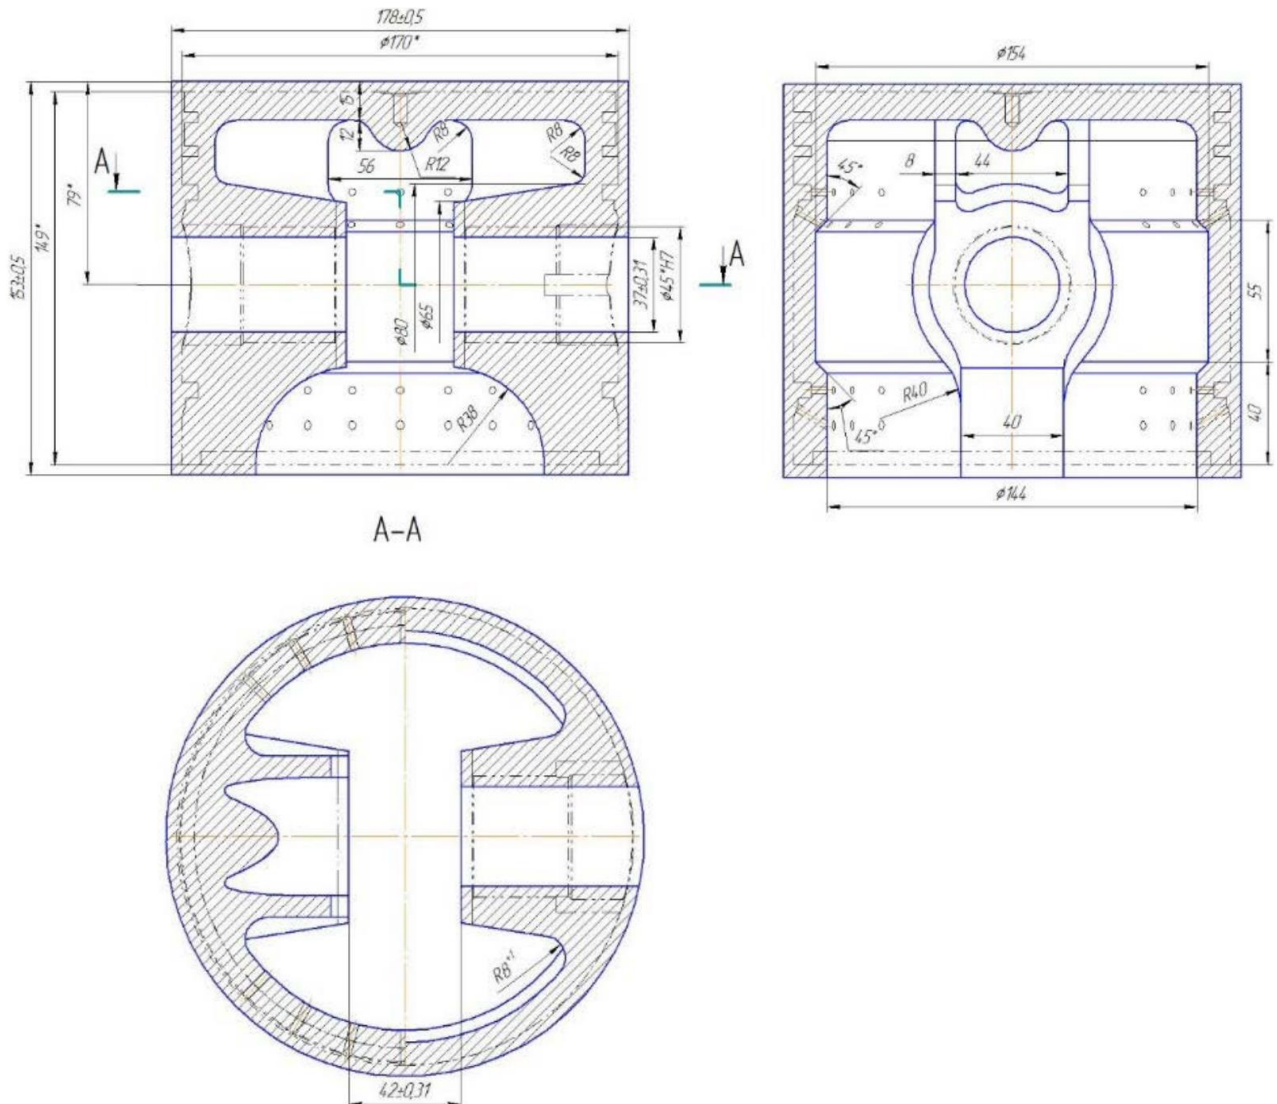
Кресленик литої заготовки деталі «Поршень»
